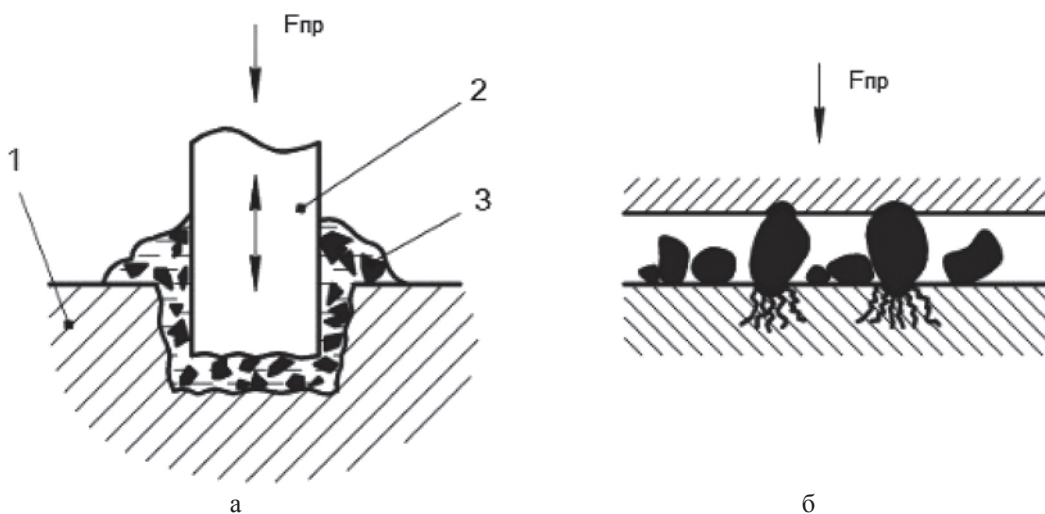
Схеми процесів різання (а) і руйнування (б) під час ультразвукової обробки крихких деталей [16]: 1 – деталь; 2 – інструмент; 3 – суспензія з абразивом
